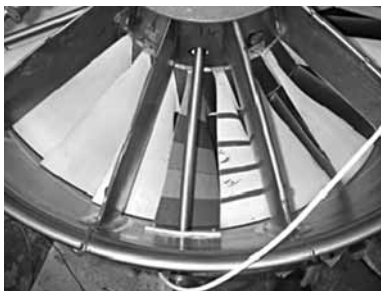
Корпус вентилятора двигателя с подготовленной лопаткой
